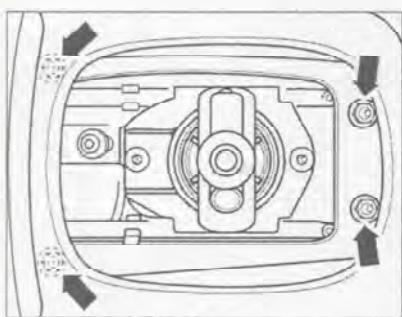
Отверните гайки (стрелки) крепления корпуса механизма переключения передач.
